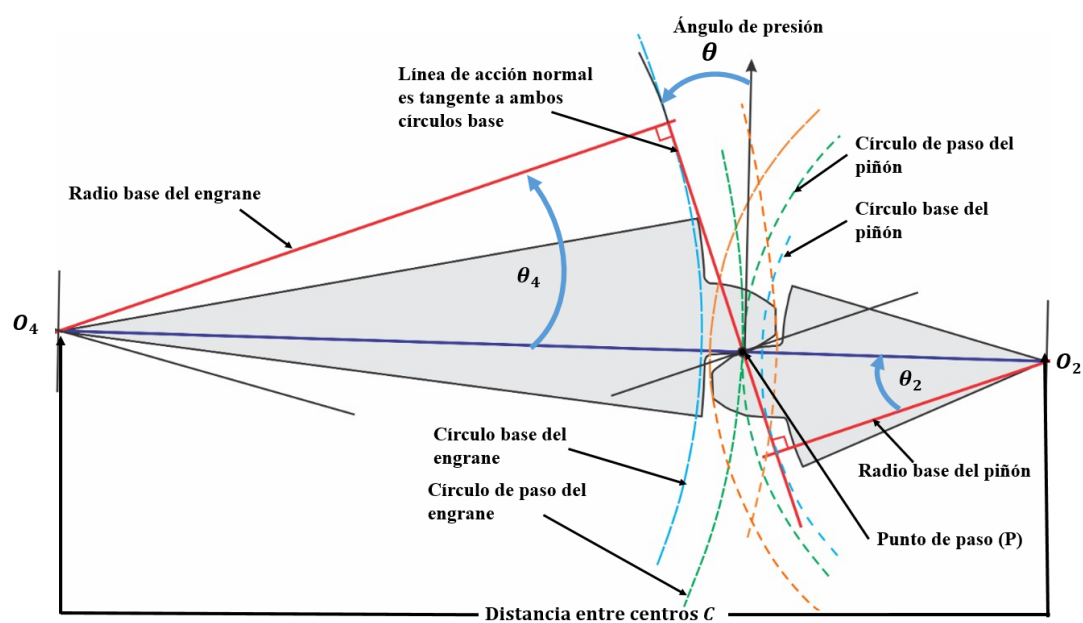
Geometría de contacto en una transmisión por engranajes cilíndricos de dientes rectos. [23]
